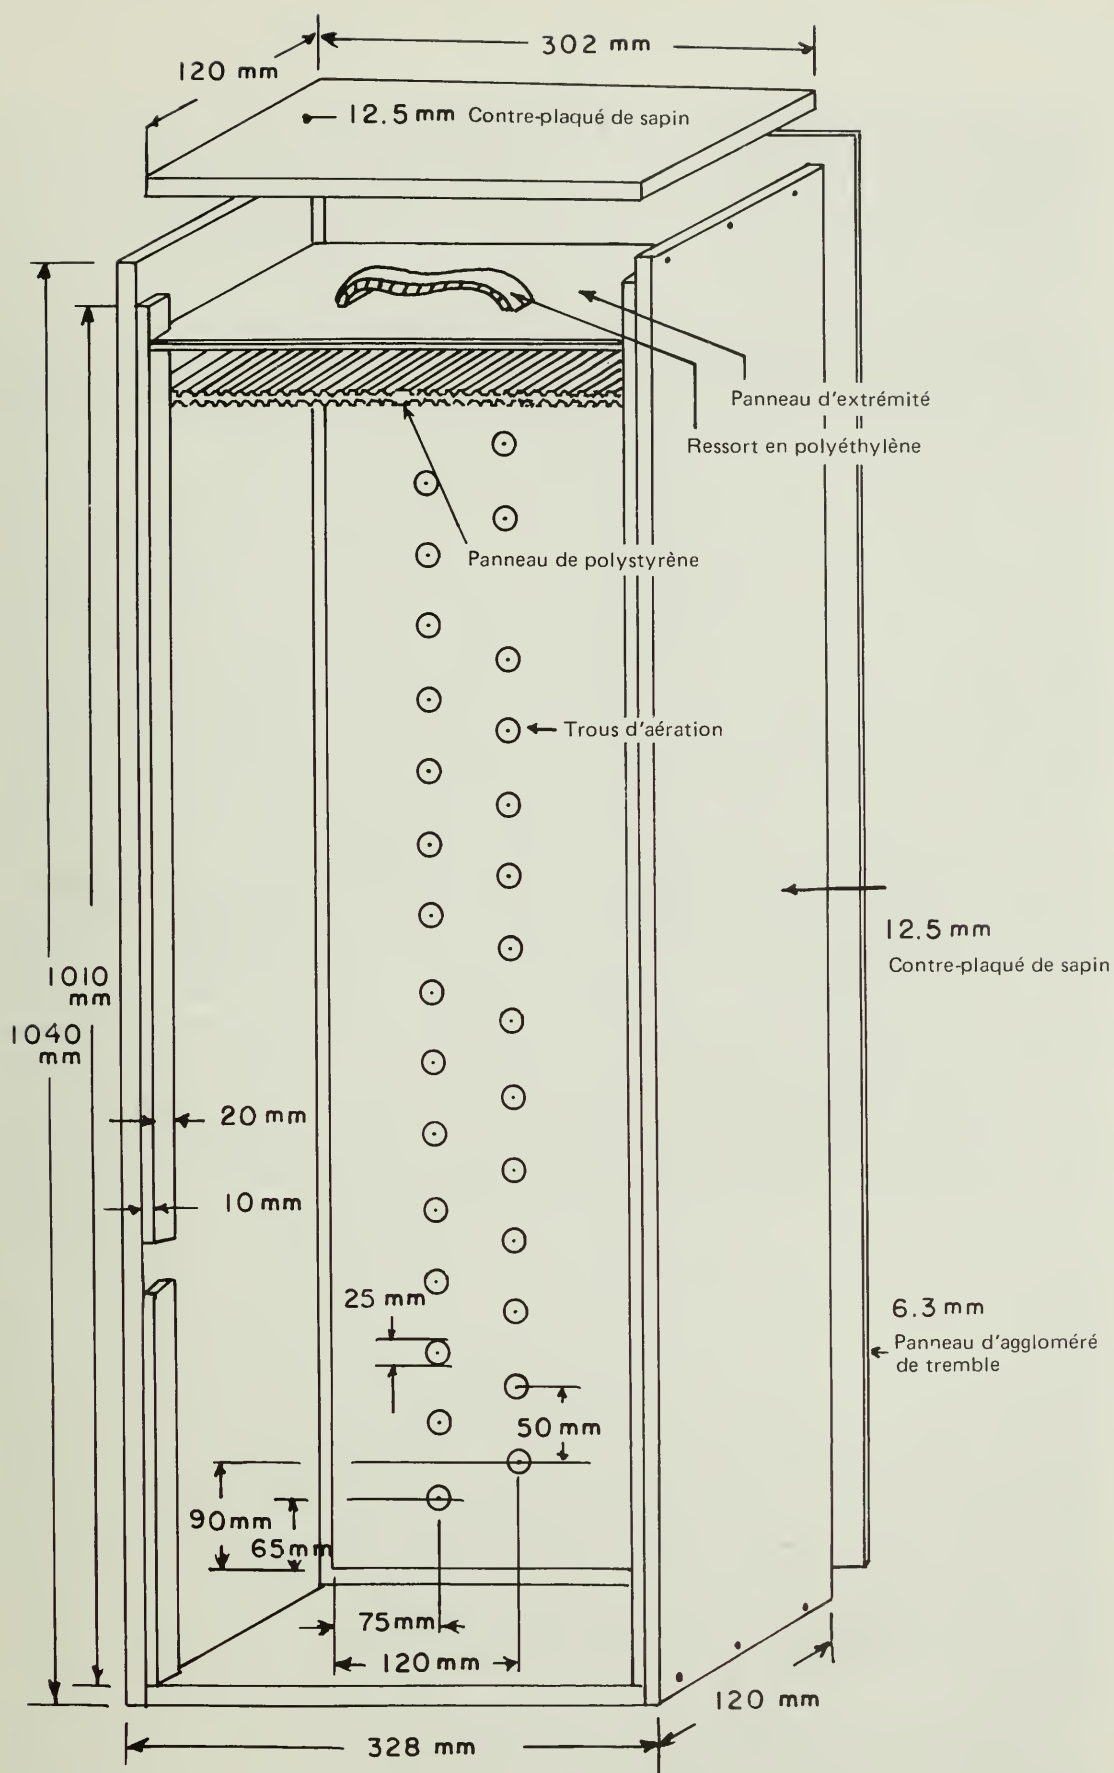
Plan d'une ruche faite de panneaux de polystyrène rainurés formant 30 tunnels.
